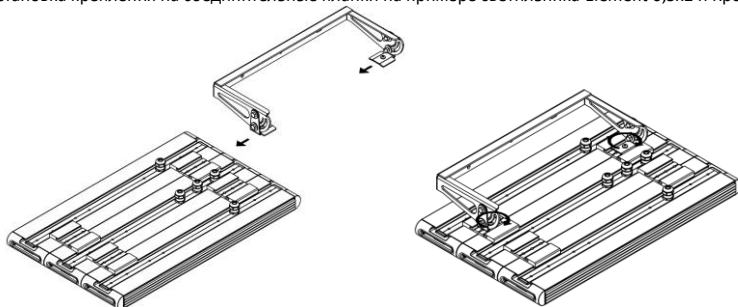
Установка крепления на соединительные планки на примере светильника Element 0,5x3 и Крепления Скоба большая с регулировкой.
